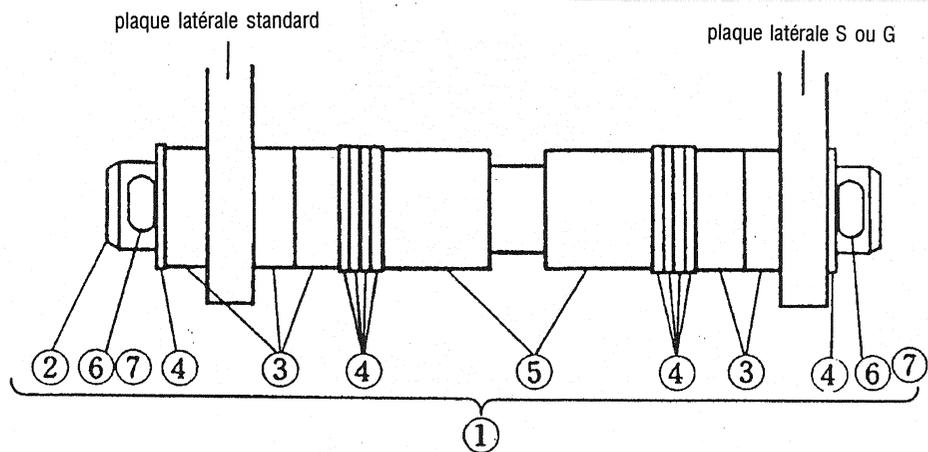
Montage de l'axe de suspension W30 (0.5-3t)
